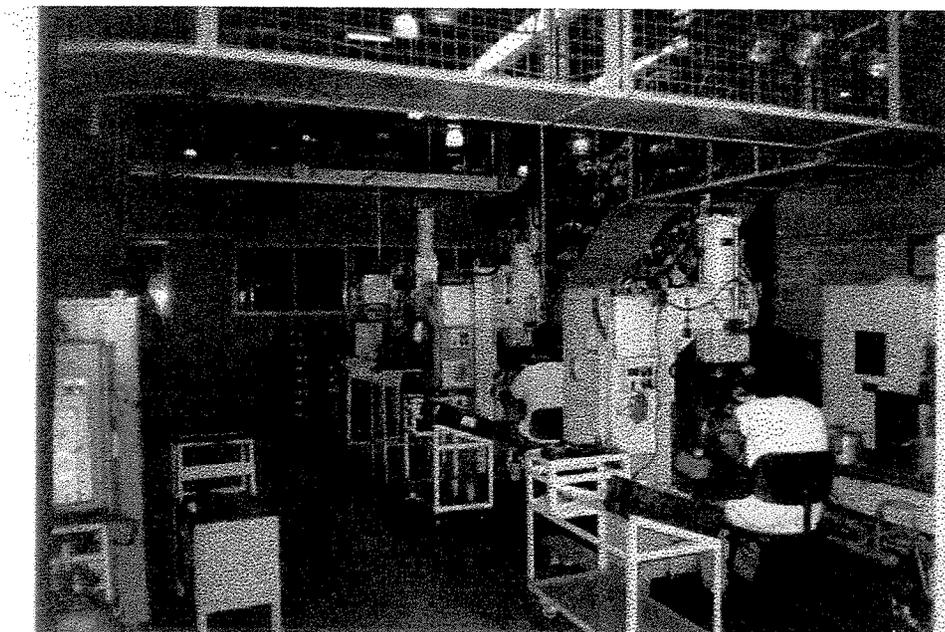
Empresa A – Corpo e Tampa – bloco 14
